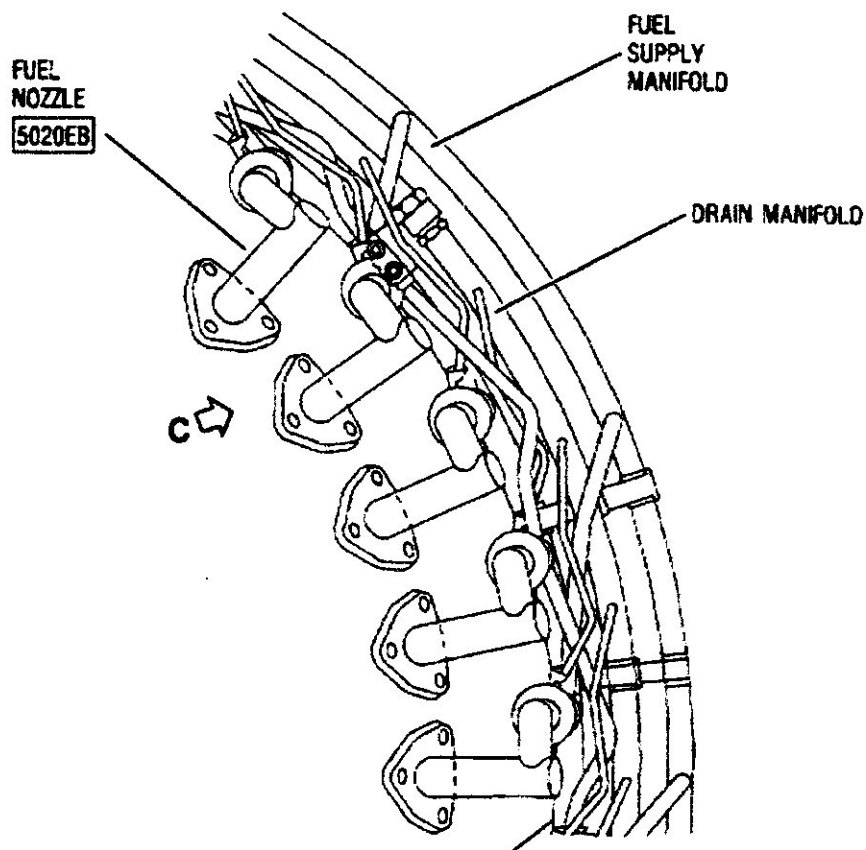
Le collecteur carburant (fuel manifold)
